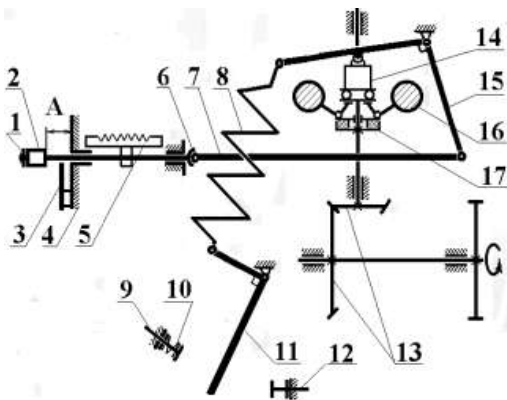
Схема регулятора КДМ: 1 - гайка; 2 - муфта регулировочная; 3 - пружина корректора; 4 - корпус ТНВД; 5 - рейка ТНВД; 6 - кольцо тяги рейки; 7 - тяга; 8 - пружина регулятора; 9 - болт минимального скоростного режима; 10 - пружина упора; 11 - рычаг управления; 12 - болт максимального скоростного режима; 13 - шестерни привода регулятора; 14 - муфта грузиков; 15 - двуплечий рычаг; 16 - грузики; 17 - демпферы.
